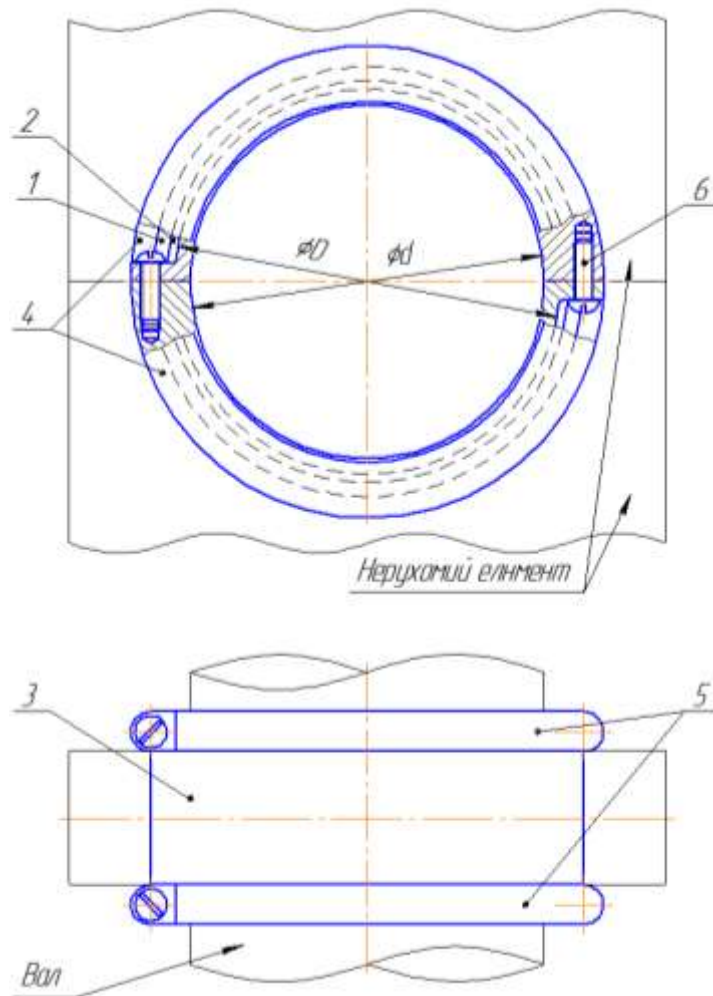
Підшипник ковзання: 1 – напівкільцеві вкладиші пластинчастої форми; 2 – антифрикційний шар, 3 – муфта; 4 – напівмуфта; 5 – реборди; 6 – з'єднувальні гвинти;  $D$  – зовнішній діаметр муфти;  $d$  – внутрішній діаметр муфти
